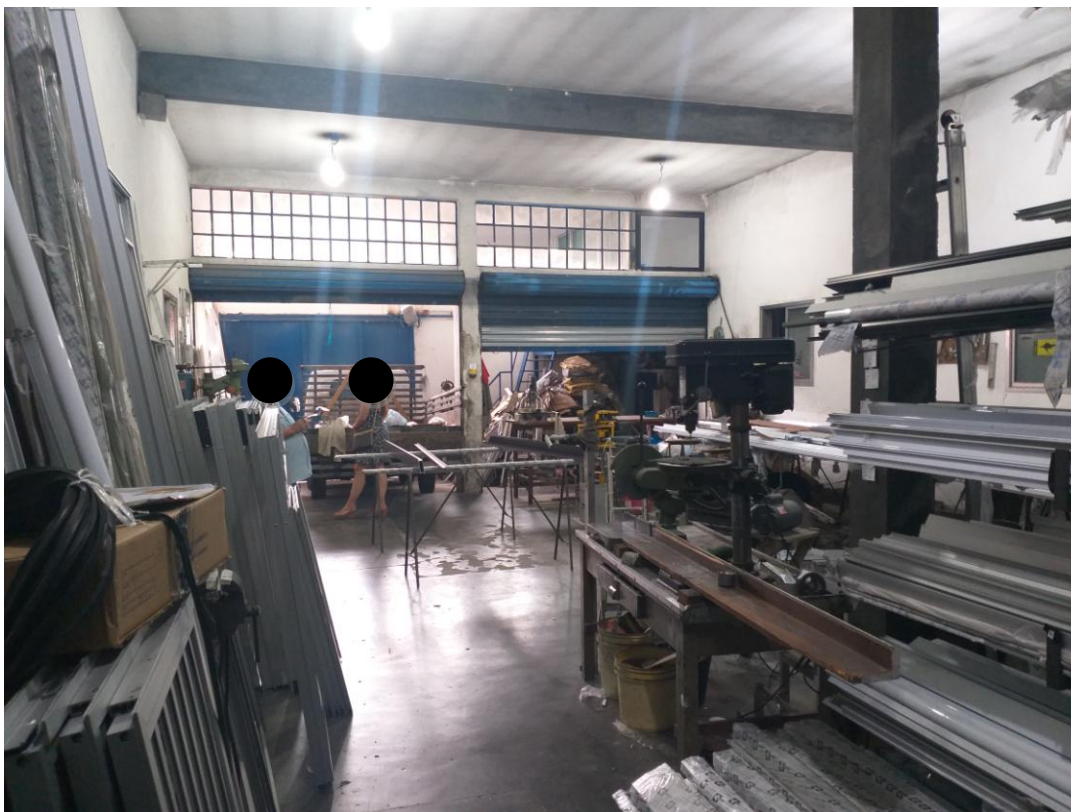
Vista interna do imóvel, da entrada do fundo para frente
